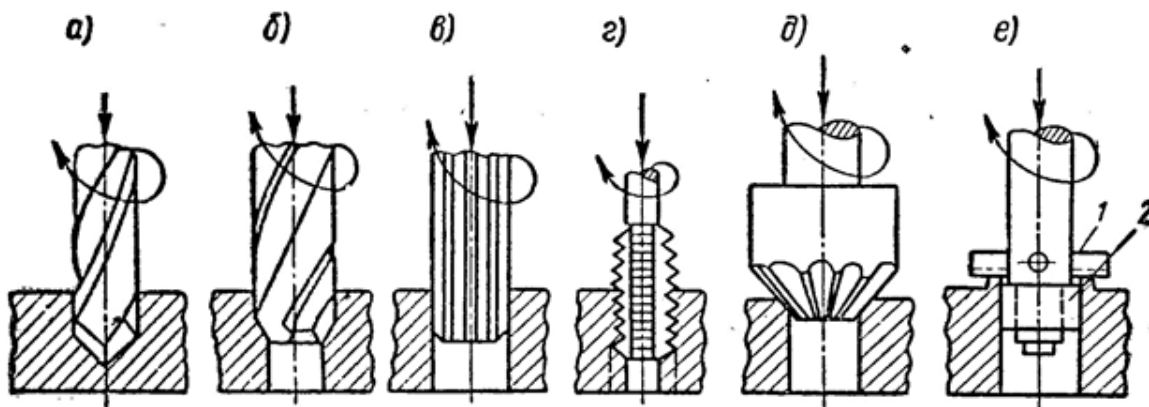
Основные виды обработки заготовок на сверлильных станках
